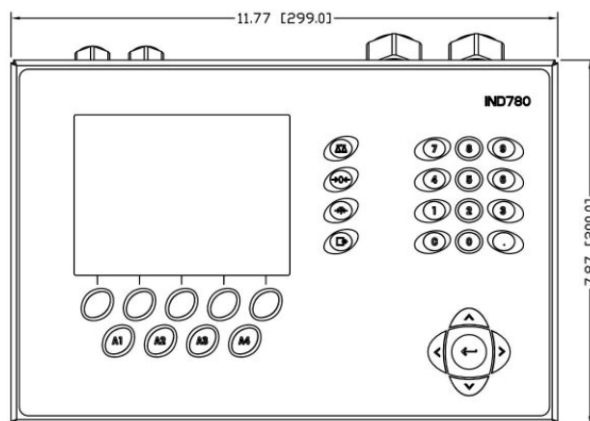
Dimensiones del terminal IND780batch con caja para ambientes adversos, vista frontal
